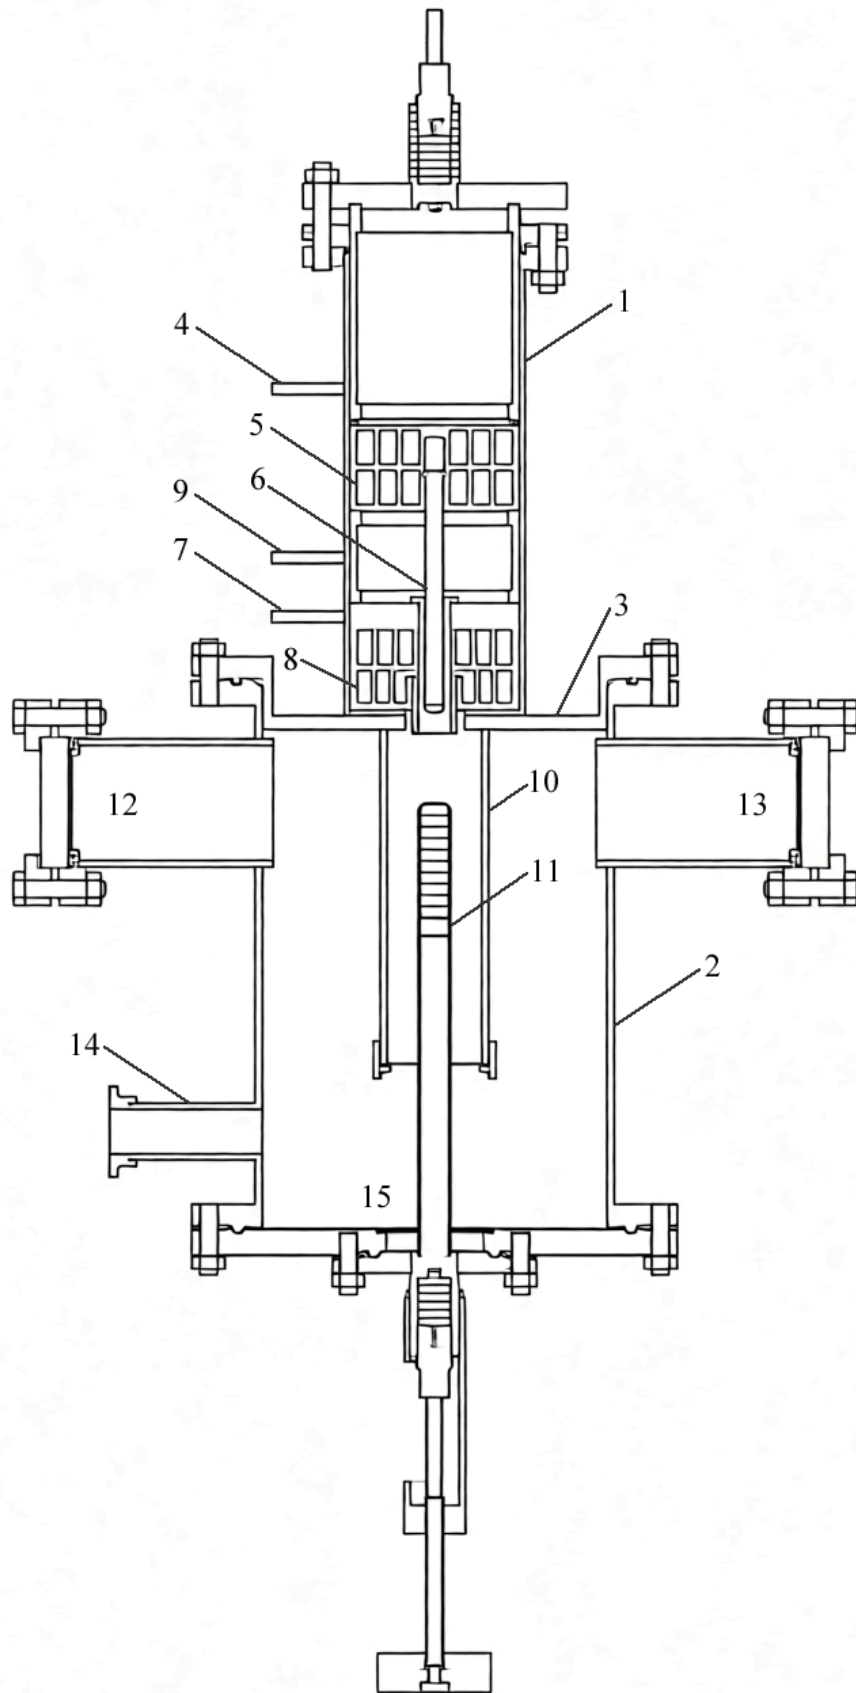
Схема реактора установки ЭУ-ЛП.
